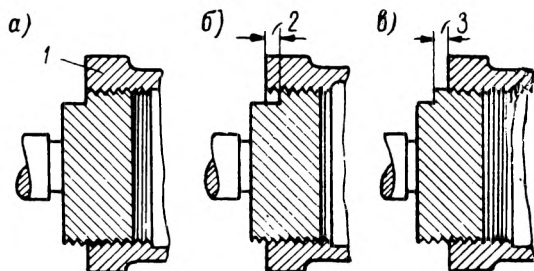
Измерение внутренней конической резьбы: а — теоретический размер; б — максимальный размер; в — минимальный размер. 1 — плоскость совпадения; 2 — на $1\frac{1}{2}$ оборота больше; 3 — на $1\frac{1}{2}$ оборота меньше.
